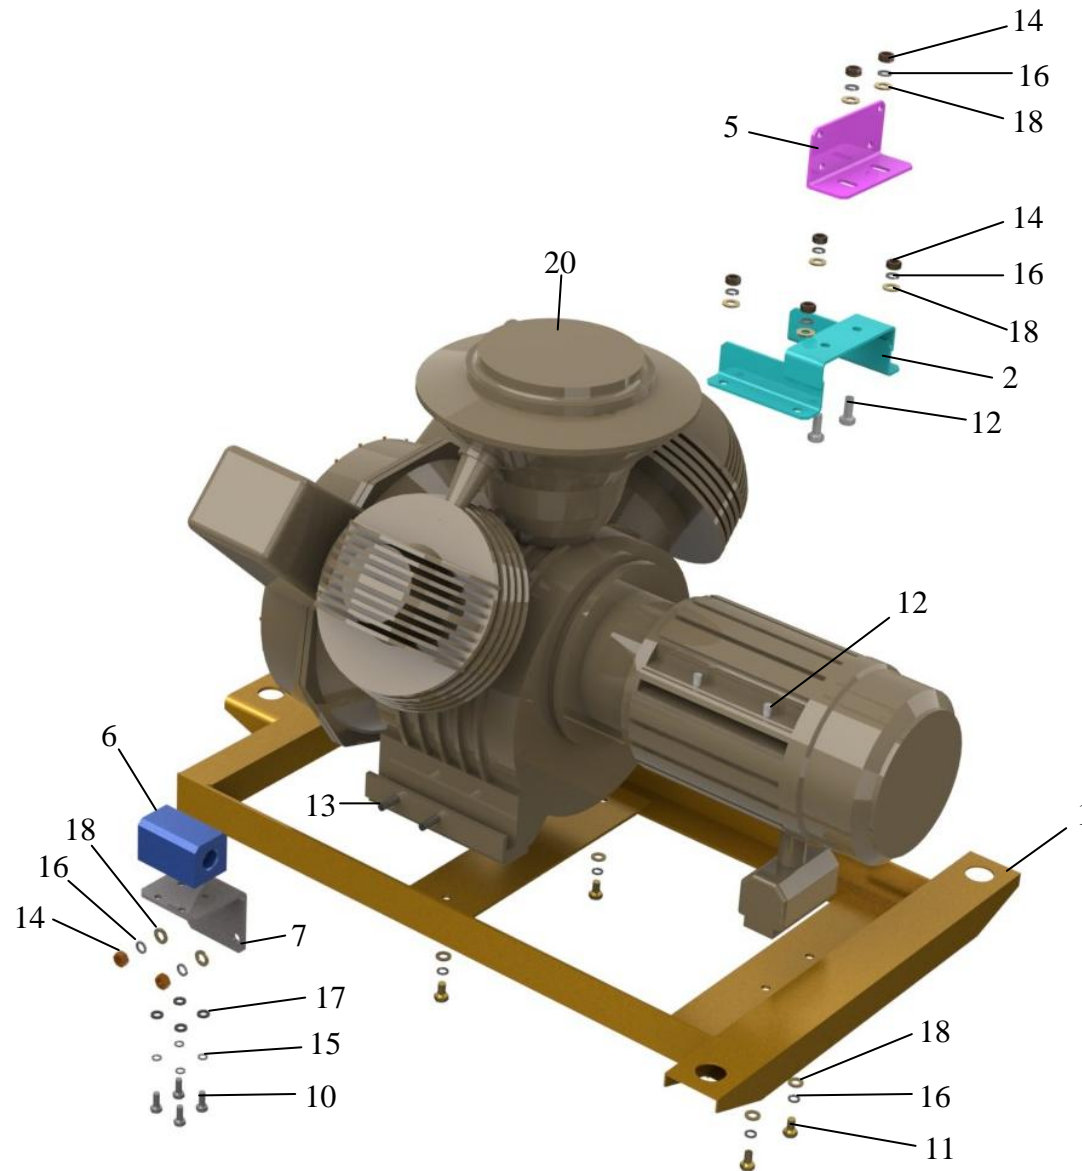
Компрессор АКСМ 32102-230301.000-10
